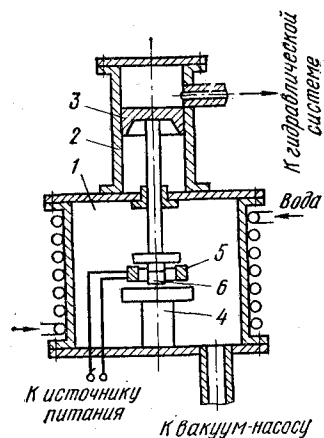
Принципиальная схема установки для диффузионной сварки в вакууме:
